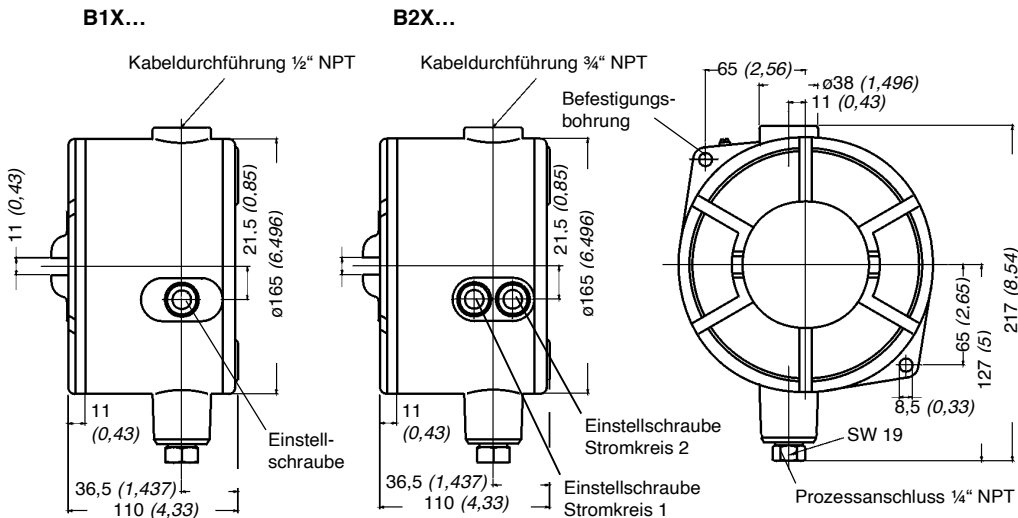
Bourdonrohr-Druckschalter Typ B1X.../B2X...
